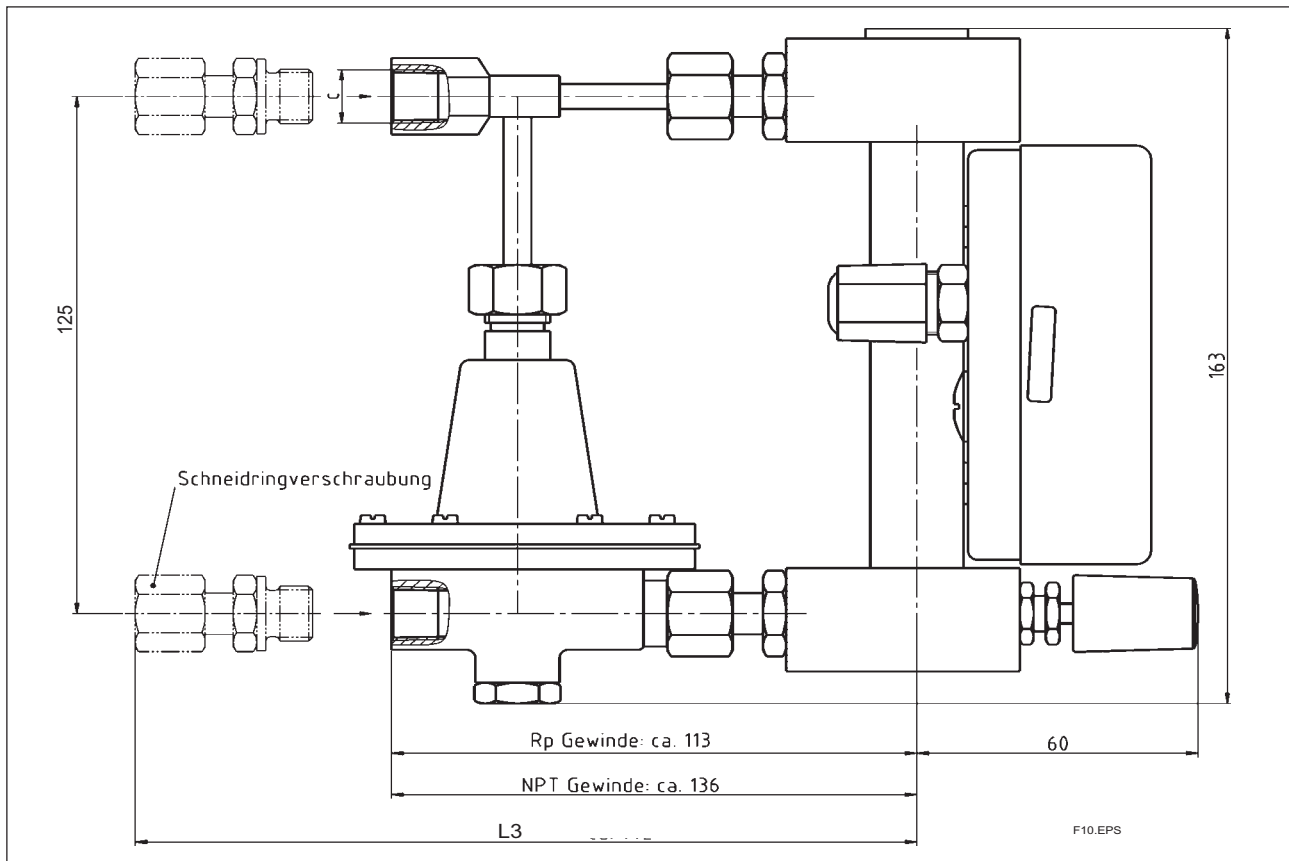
Ausführung mit Ventil im Eingang und Vordruckregler
